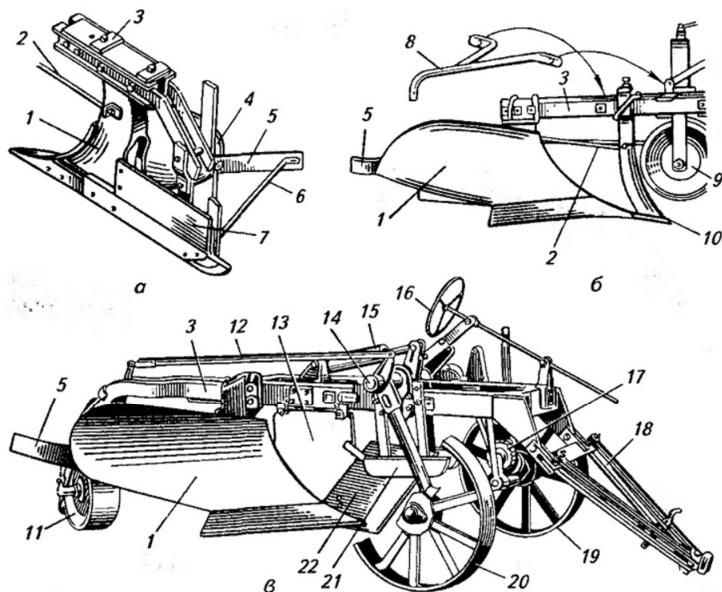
Кустарниково-болотные плуги: а — корпус плуга; б—плуг ПБН-75; в — плуг ПКБ-75; 1 — корпус; 2, 6 — раскосы; 3 — рама; 4 — отвал; 5 — перо; 7 —
